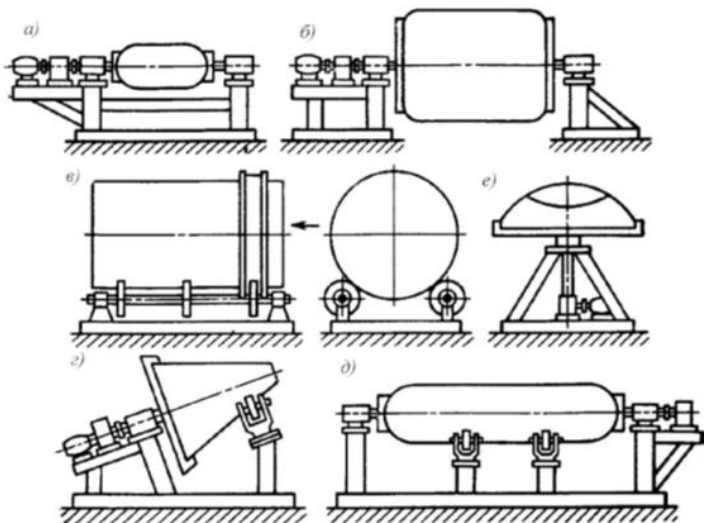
Схемы вращателей для сварки кольцевых швов
